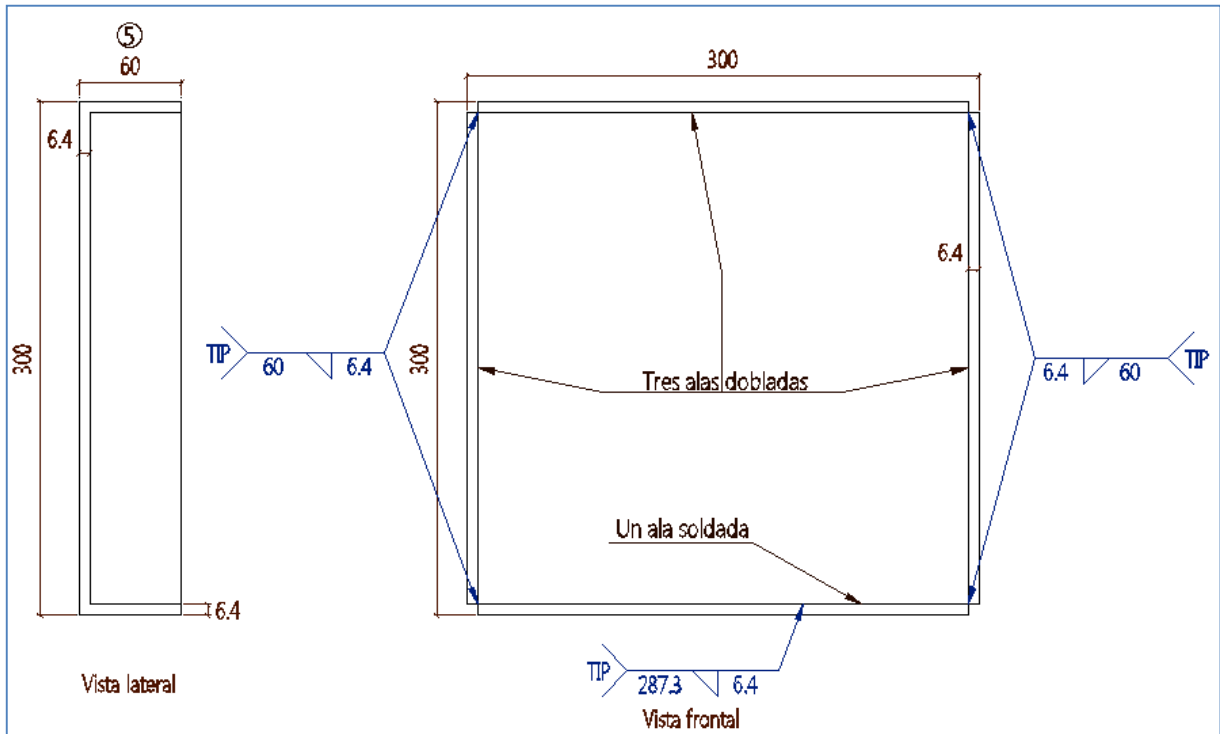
Detalle despiece pieza No.5 modelo 2 tensión.
